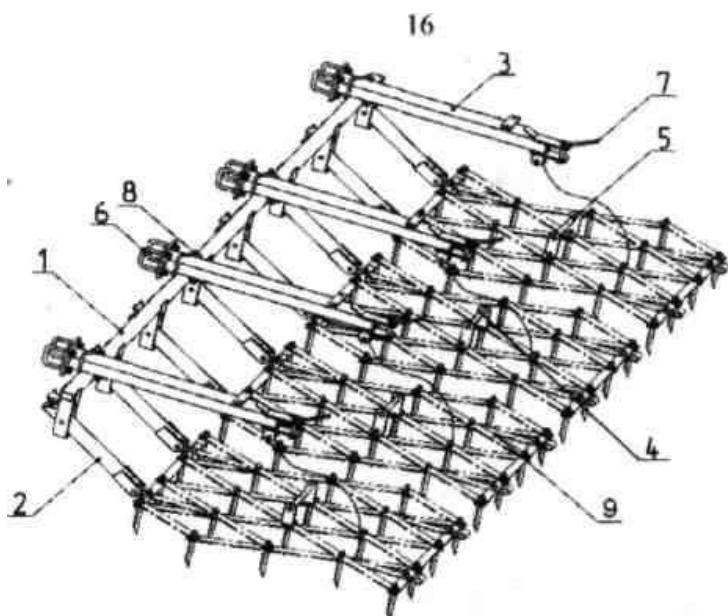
Приспособление для навешивания борон типа БЗСС-1
